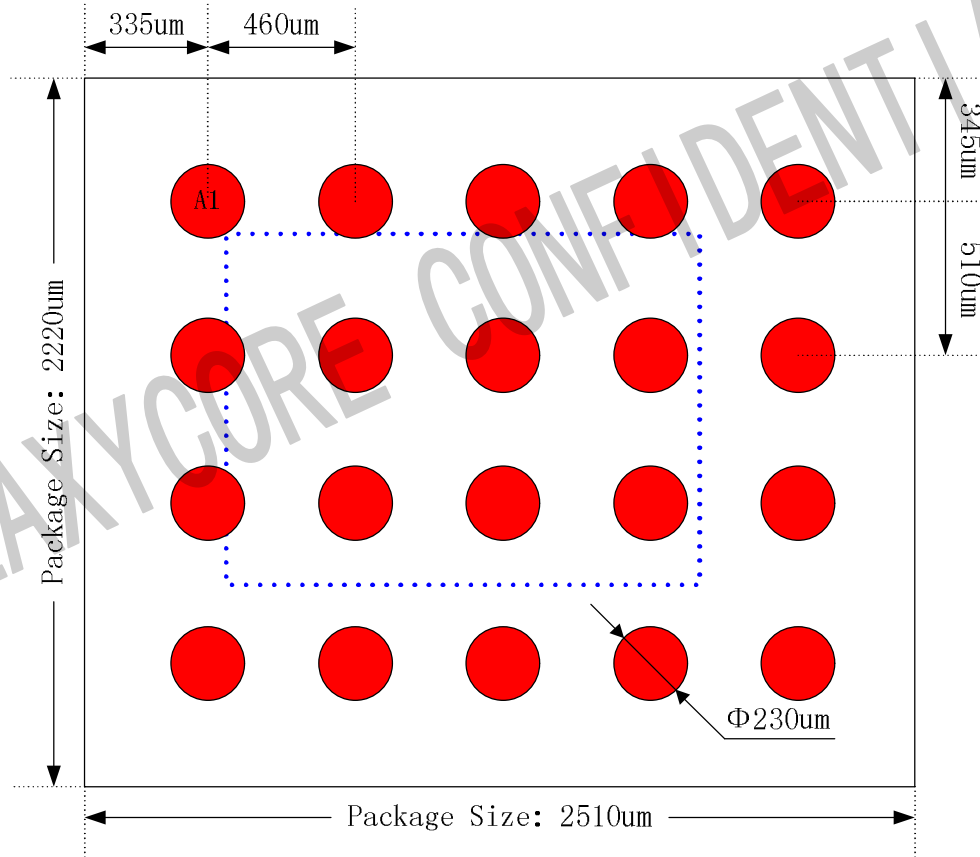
PCB 焊盘设计说明示意图(Top View)
